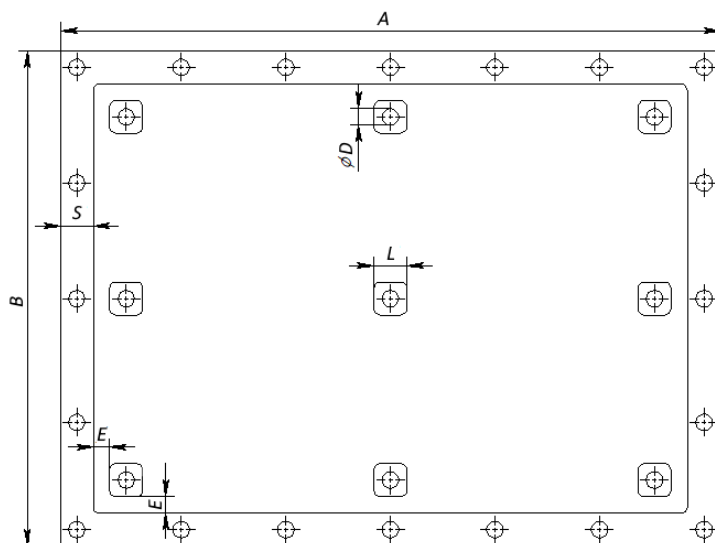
Чертеж корпусной детали с отверстиями и бобышками
